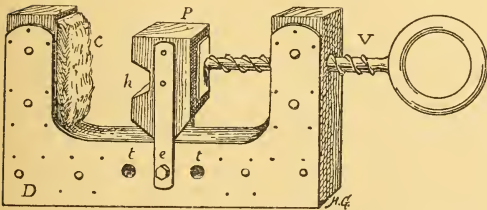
Serre-joints muni d'un taquet pour tuteur en fer.
